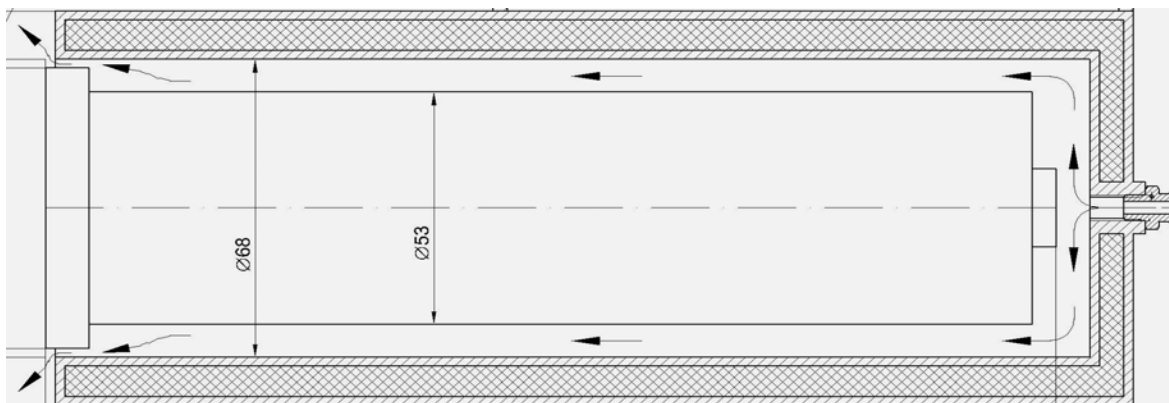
Внешний вид конструкции термокожуха для СКИ «Агат-222»
